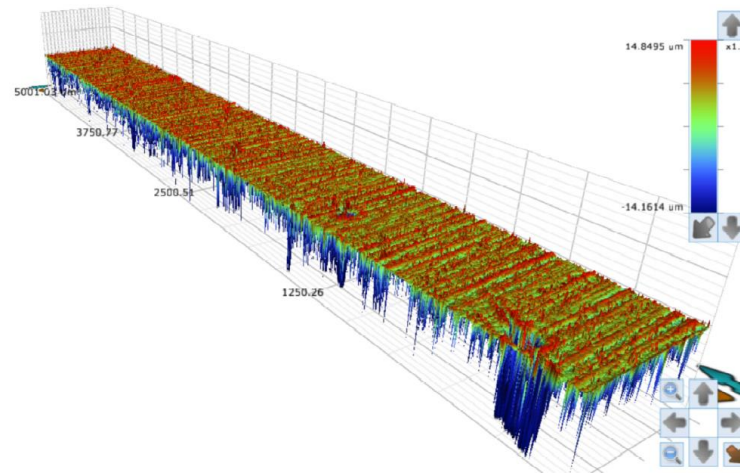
Vista 3D da superfície de medição de rugosidade da serra Fabricante 2.
